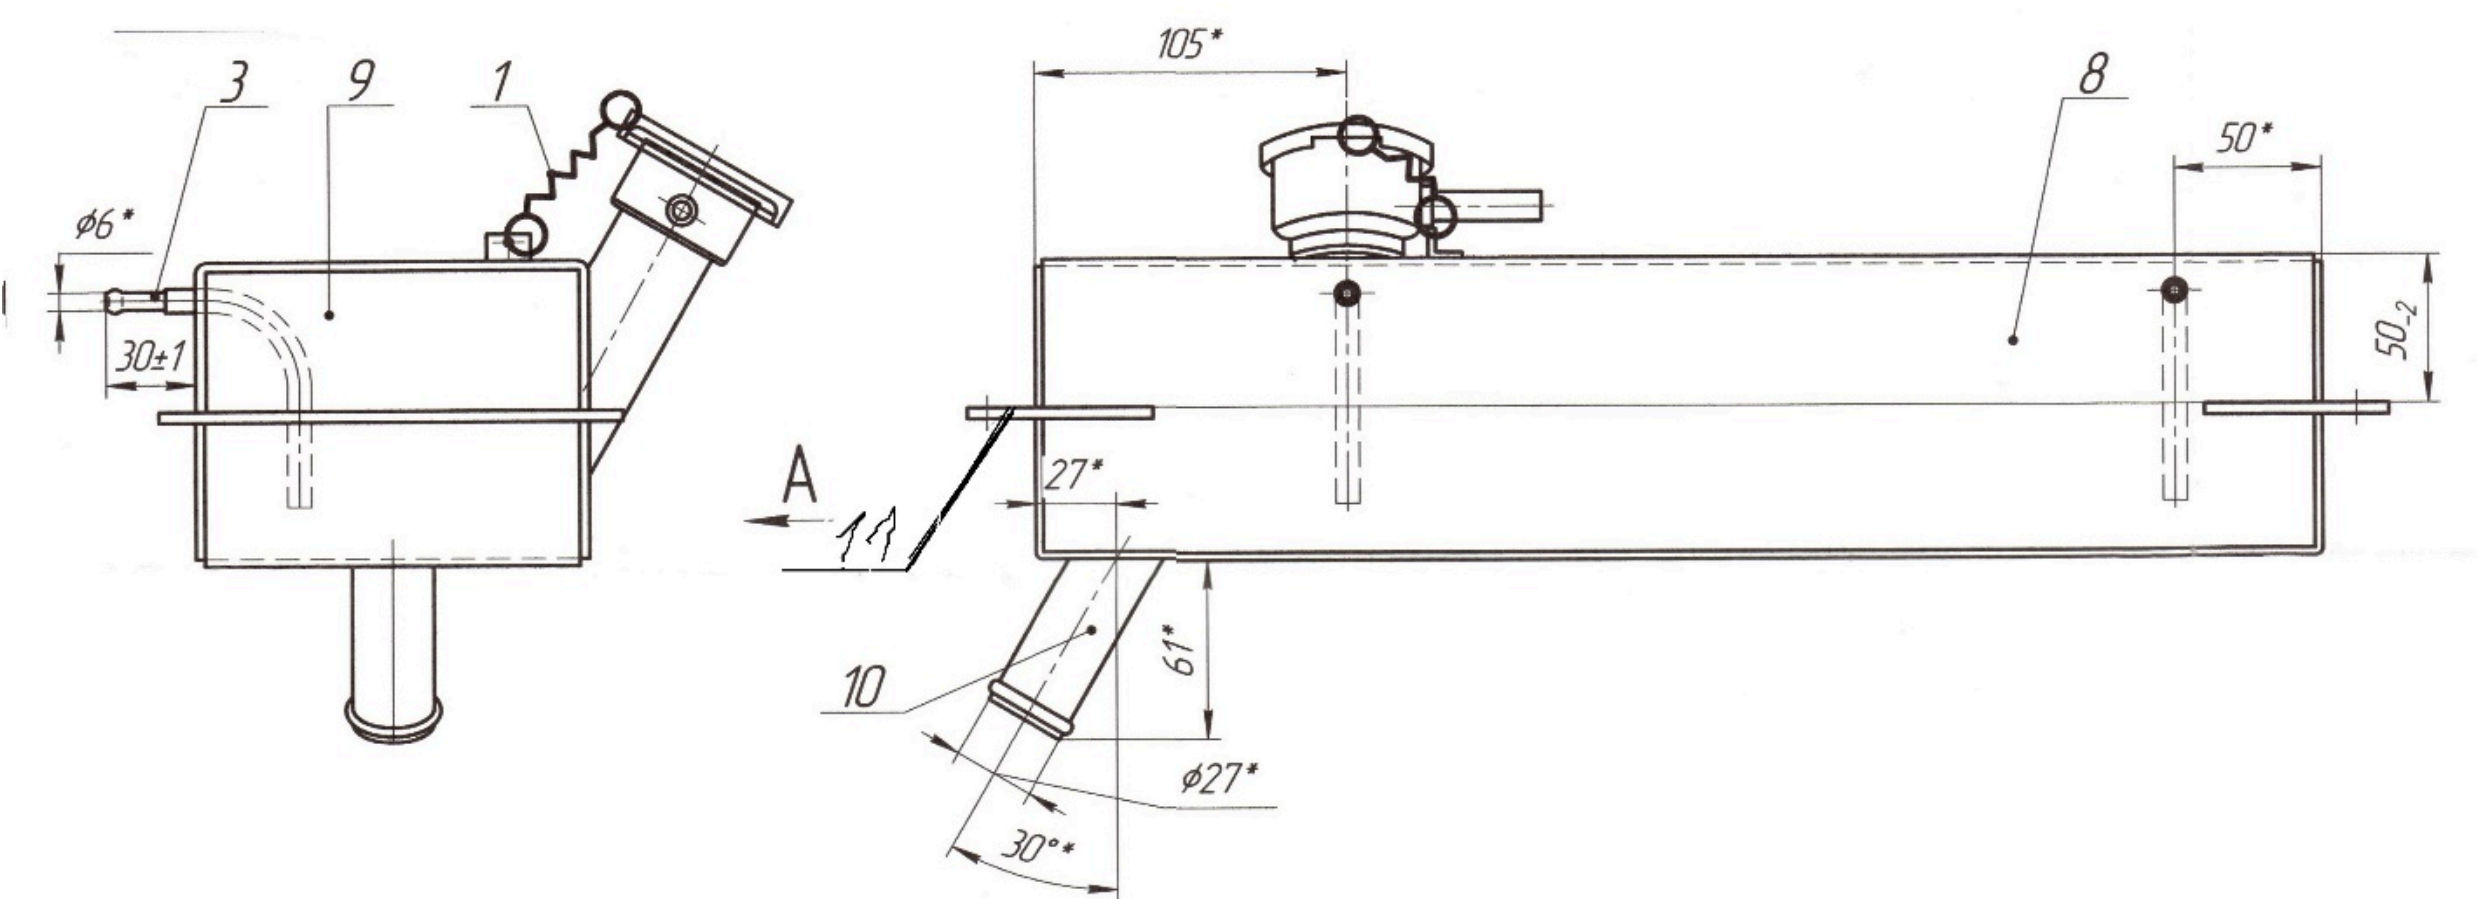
Розширювальний бачок: 8 – кришка бачка верхня; 9 – кришка бачка нижня; 3 – трубка; 10 – патрубок; 11 – опора
